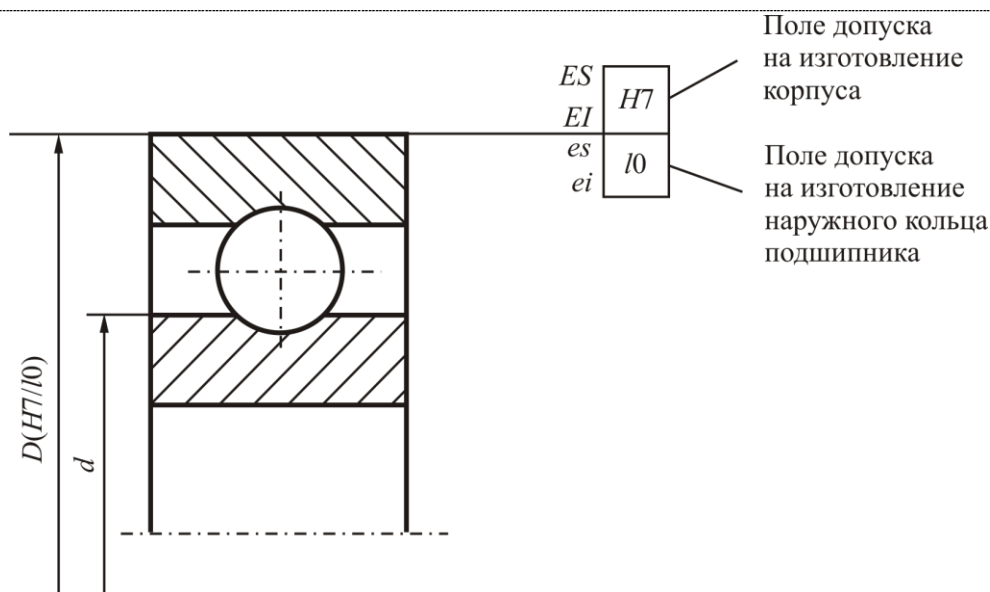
Схема расположения полей допусков в соединении наружного кольца подшипника с корпусом (для примера рассмотрена посадка $\frac{H7}{l0}$)
